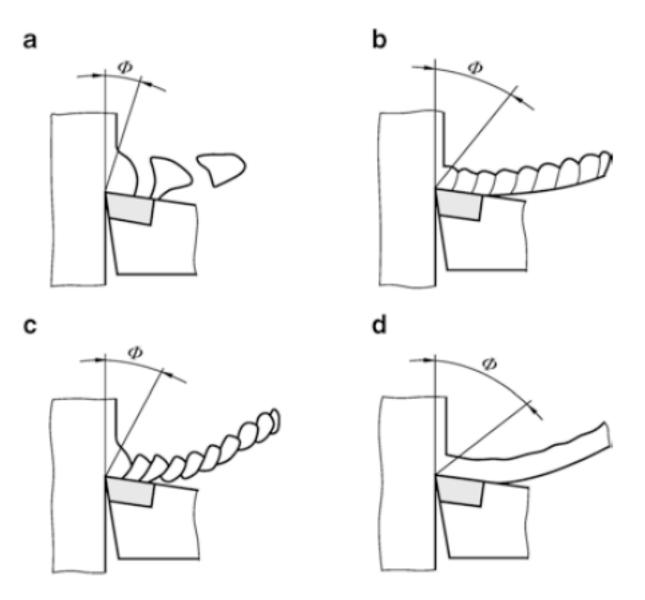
Spanarten: a Reißspan, b Scherspan, c Lamellenspan, d Fließspan
